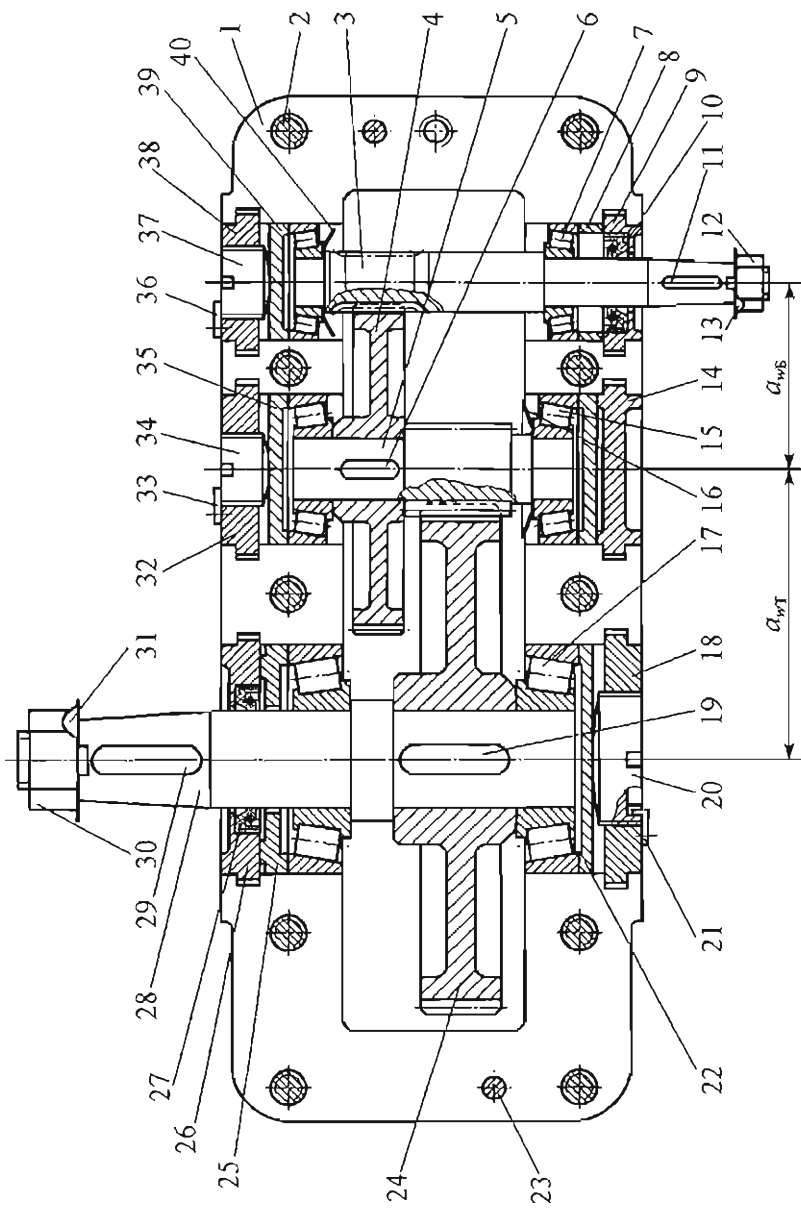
Конструкция двухступенчатого цилиндрического редуктора, выполненный по развернутой схеме
